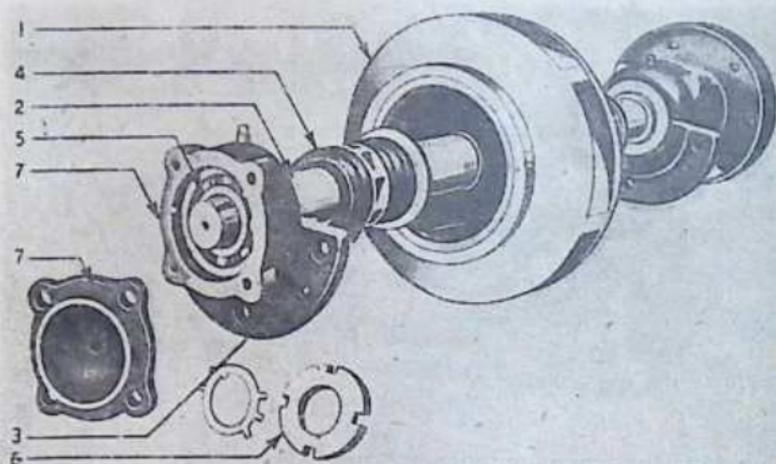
Части колеса и вала насоса (в разобранном виде): 1— колесо насоса, 2— шлифованный стальной вал; 3— кольцо водяного затвора, 4— прокладка, 5— стандартный шарикоподшипник, 6— закрепная гайка, 7— станина и предохранительная коробка для шарикоподшипников.
